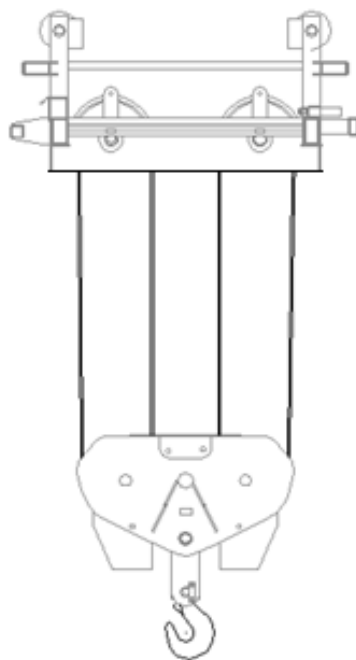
Detalle reenvíos cable entre gancho y carro
